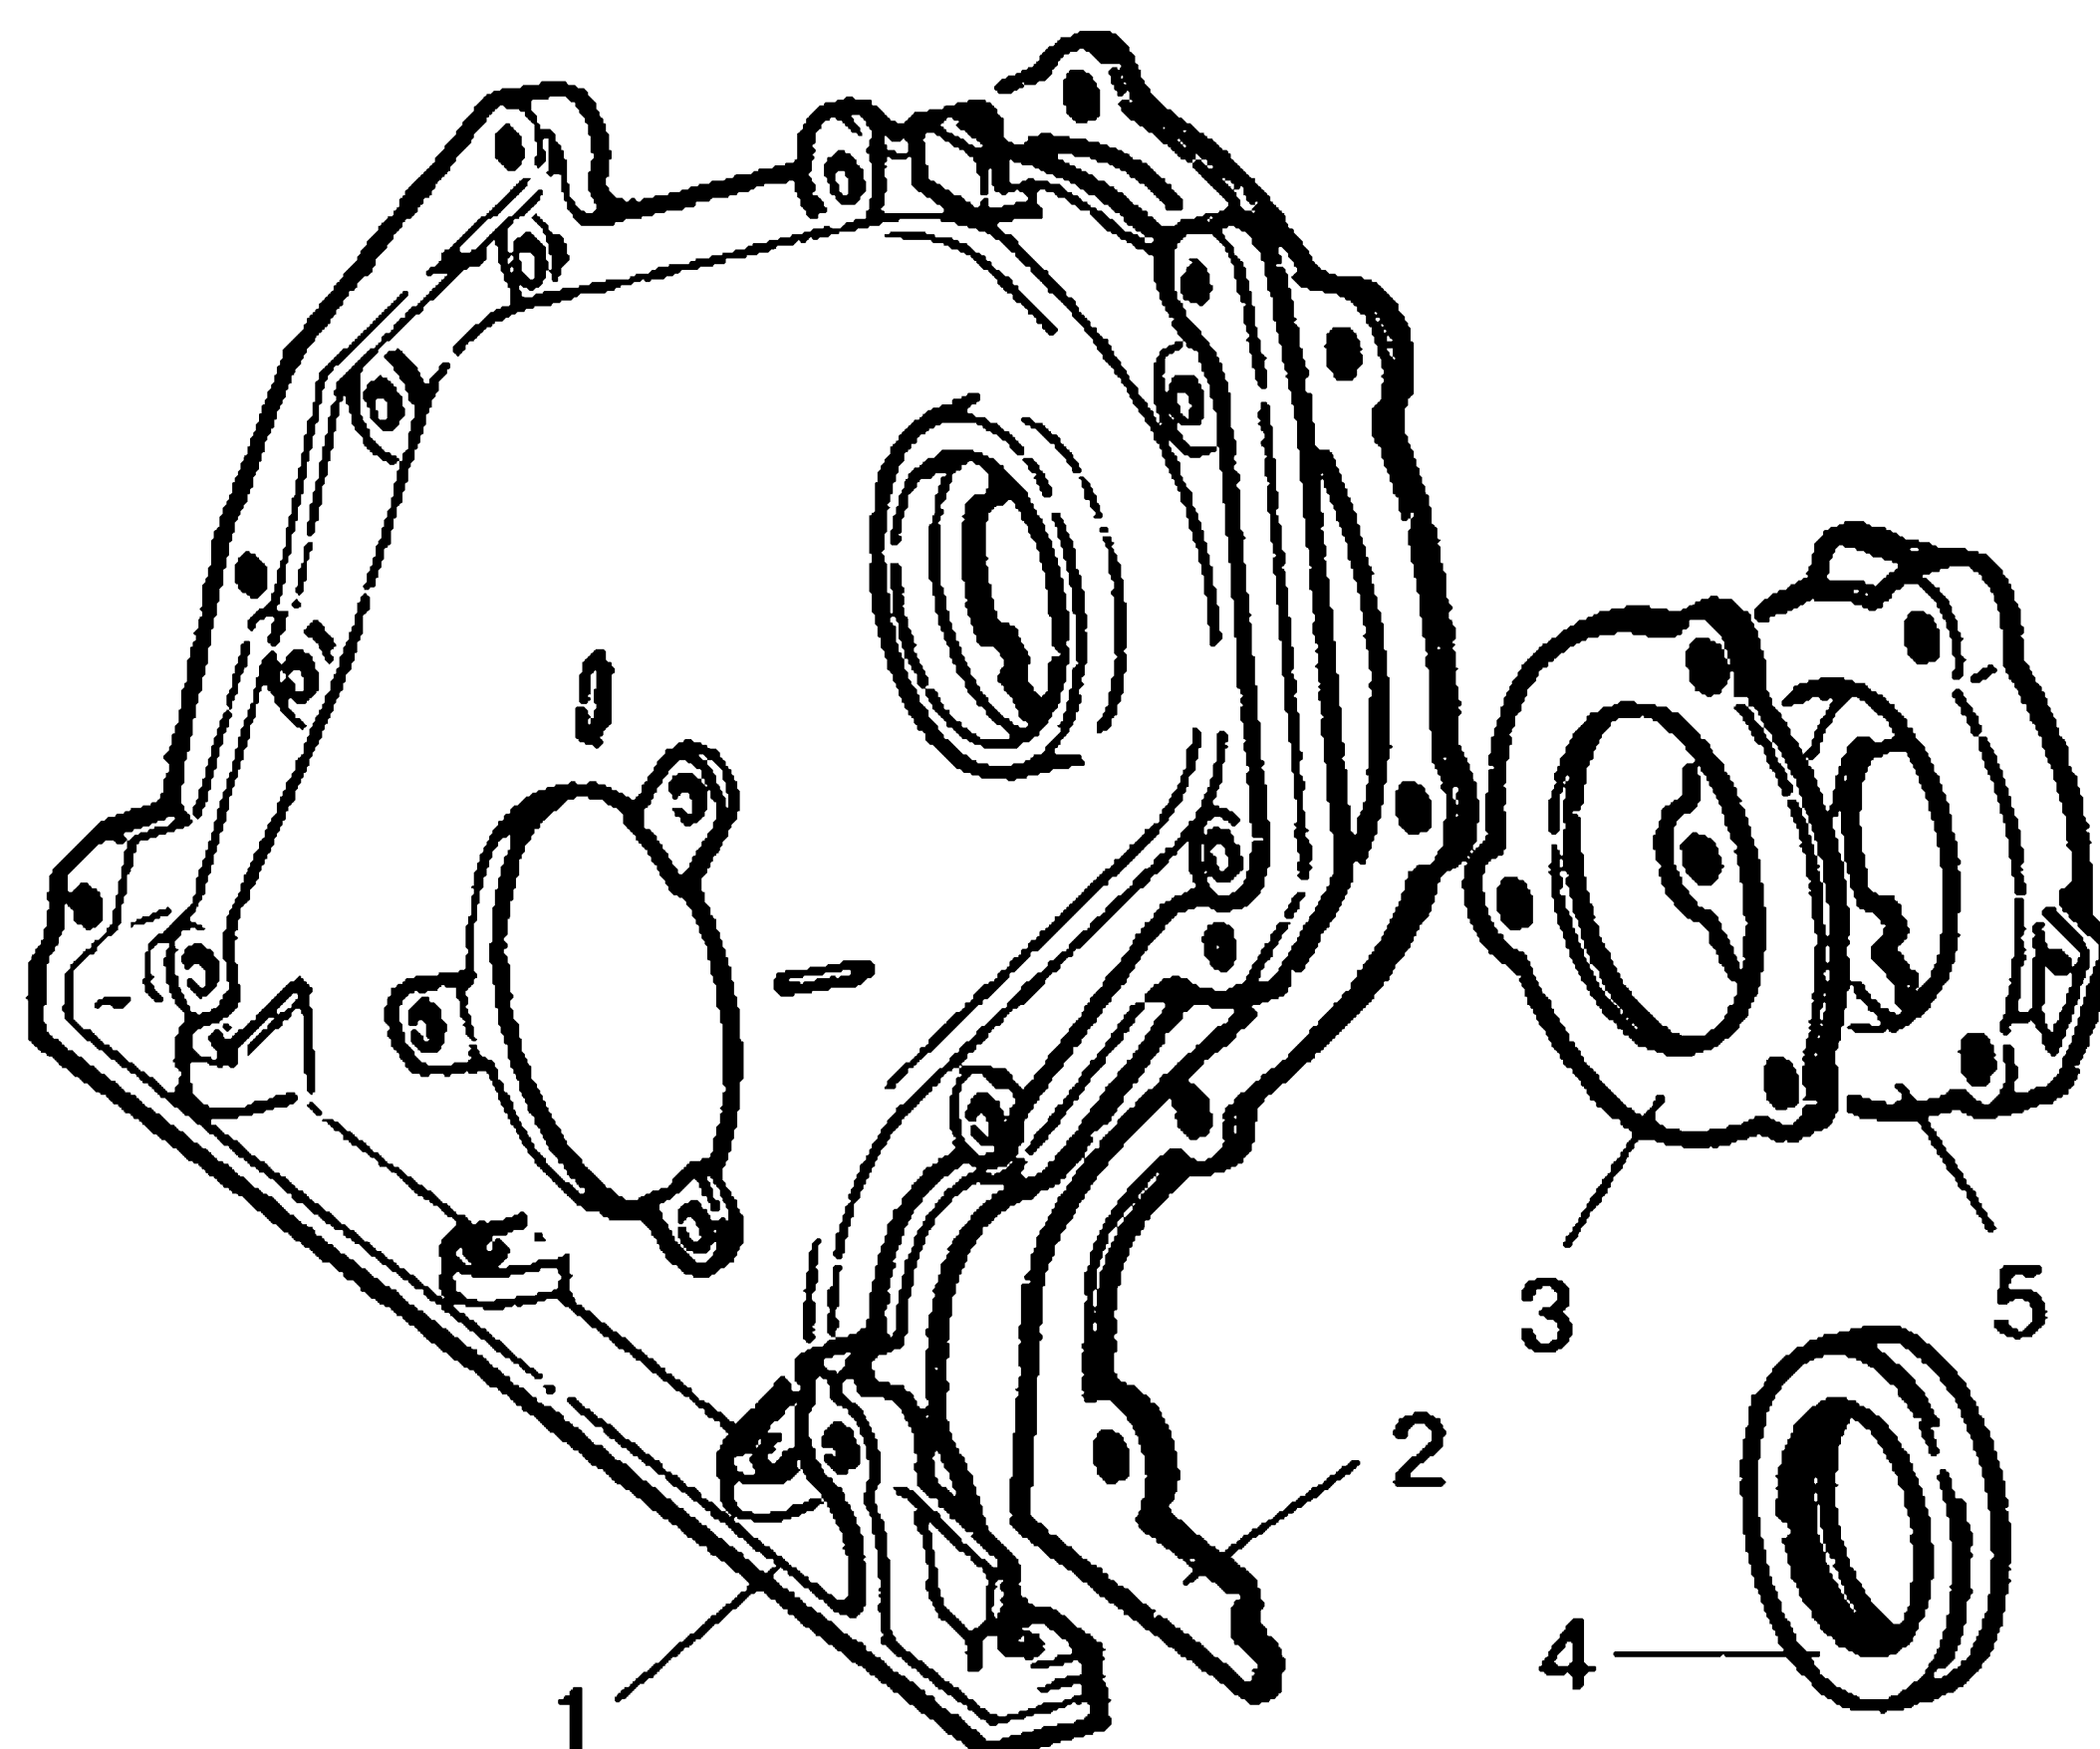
Задняя крышка привода распределителя (1), прокладки (2 и 3), передний сальник коленвала (4) и держатель сальника (5)
